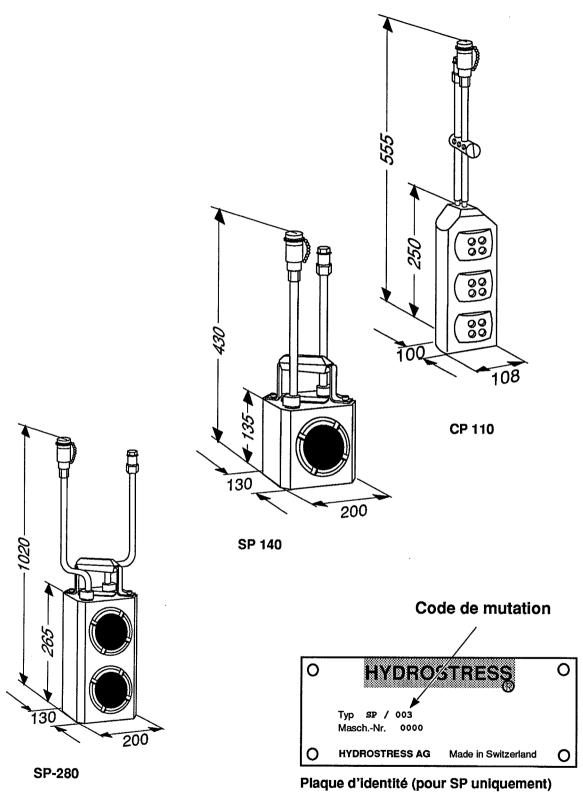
Dimensions, plaque d'identité des éléments de poussée
